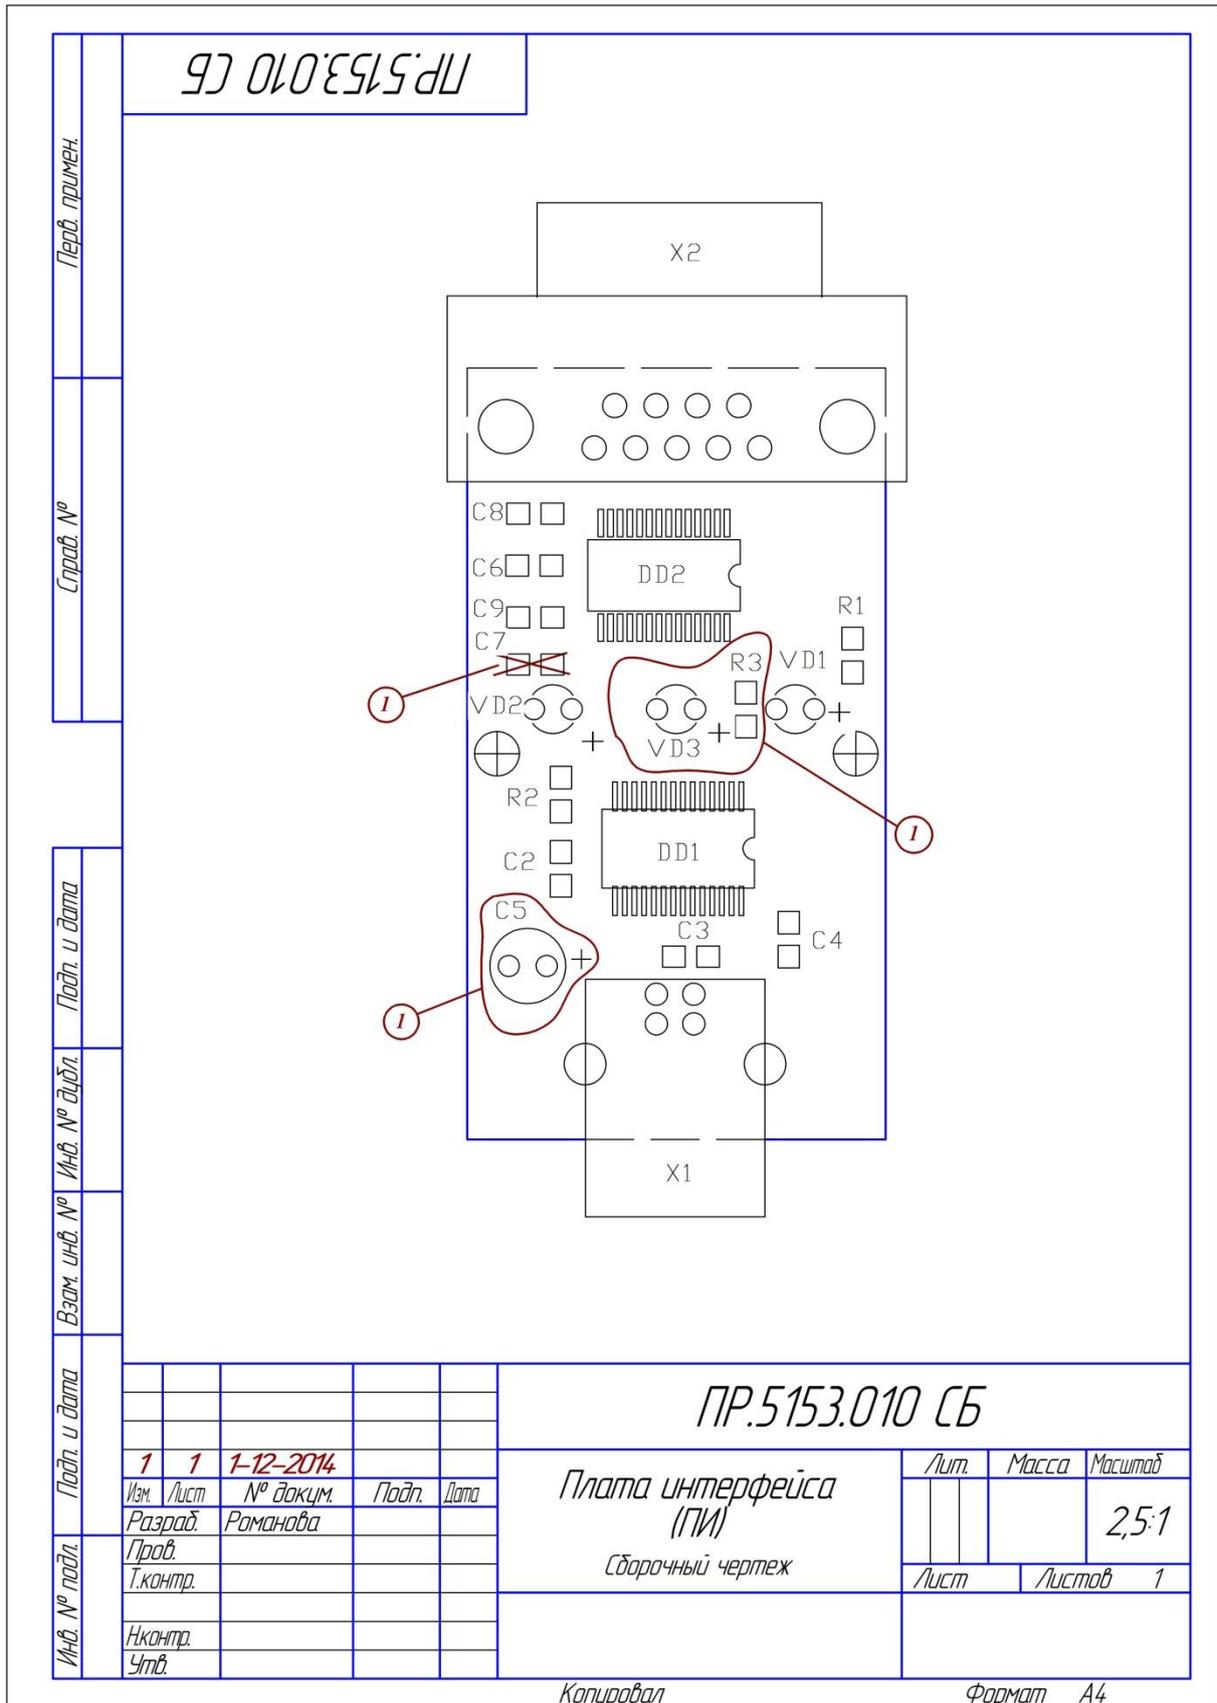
Сборочный чертёж платы с внесёнными изменениями
